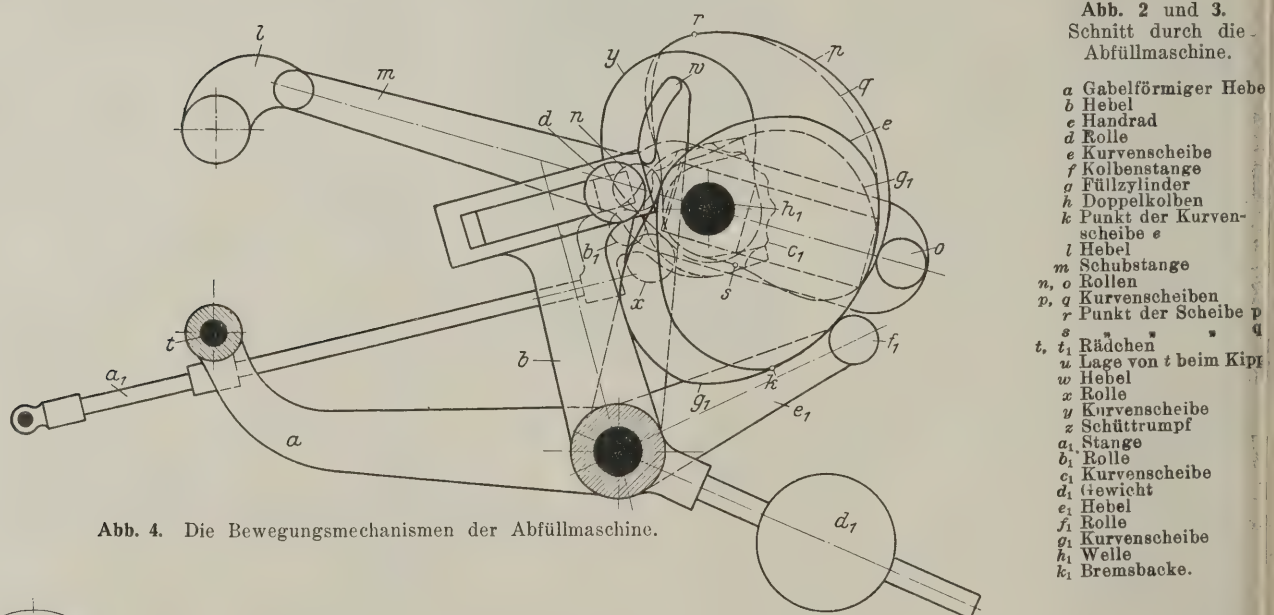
Die Bewegungsmechanismen der Abfüllmaschine.
